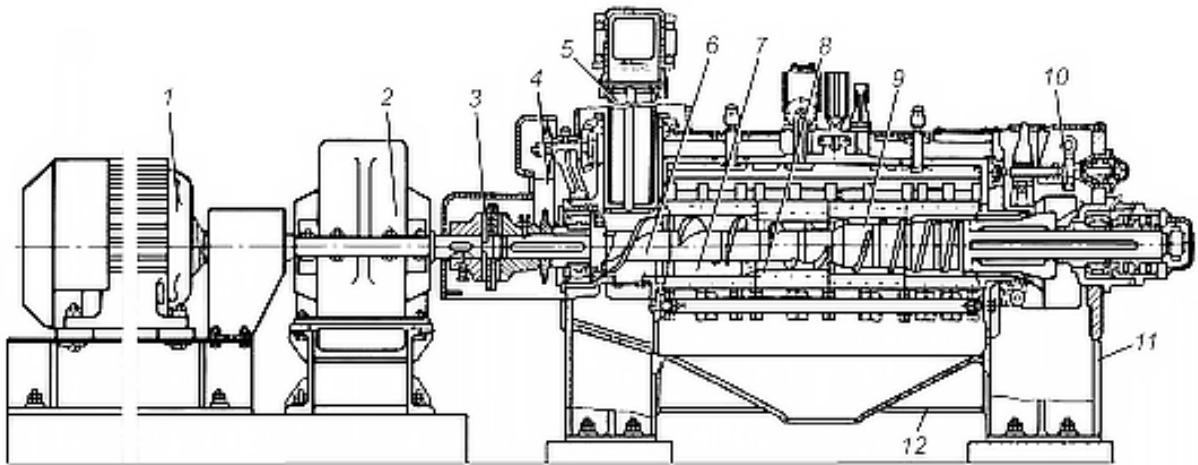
Схема олійного преса МП-68: 1 – електродвигун; 2 – редуктор; 3 – муфта; 4 – ланцюгова передача; 5 – живильник; 6 – шнековий вал; 7 – зерна камера; 8 – шнековий виток; 9 – перехідне кільце; 10 – регулятор тиску; 11 – станина; 12 – збірний пристрій.
